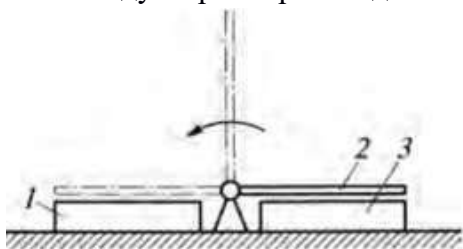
Схема устройства для сборки и сварки ферм
